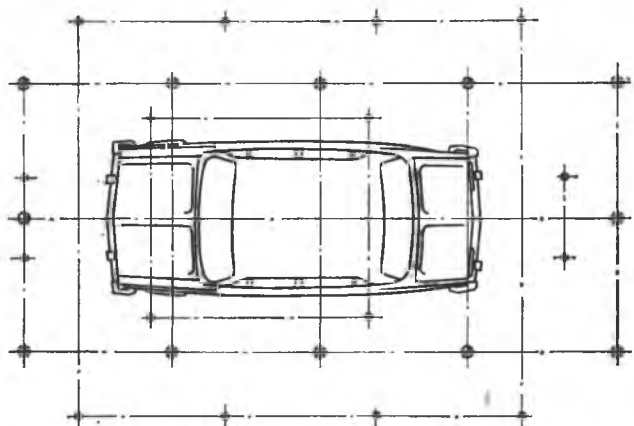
Основные узлы стенда БС-132.000 и приспособления для правки и закрепления кузовов:
